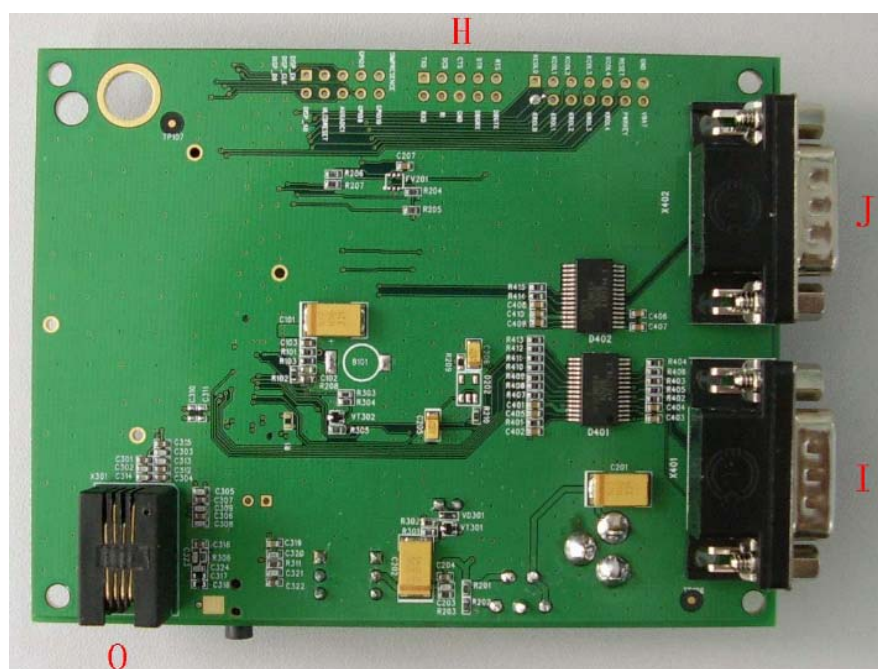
Внешний вид отладочной платы с обратной стороны
